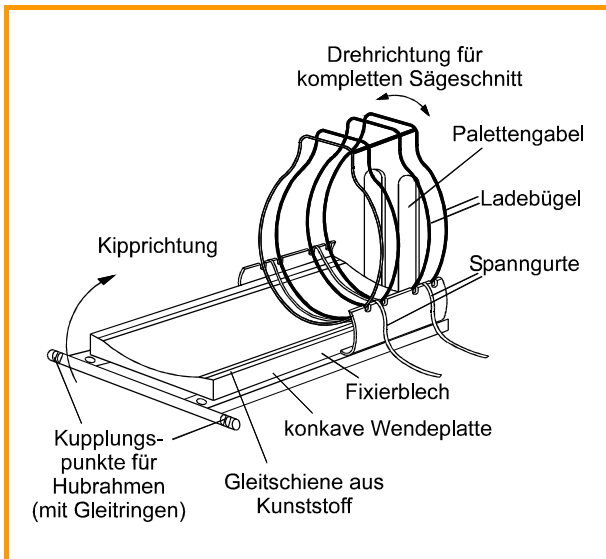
Stückholzbindeapparat, hier mit Wendepalette für einen Schlepperanbau-Hubrahmen (nach IBW /3-22/)
